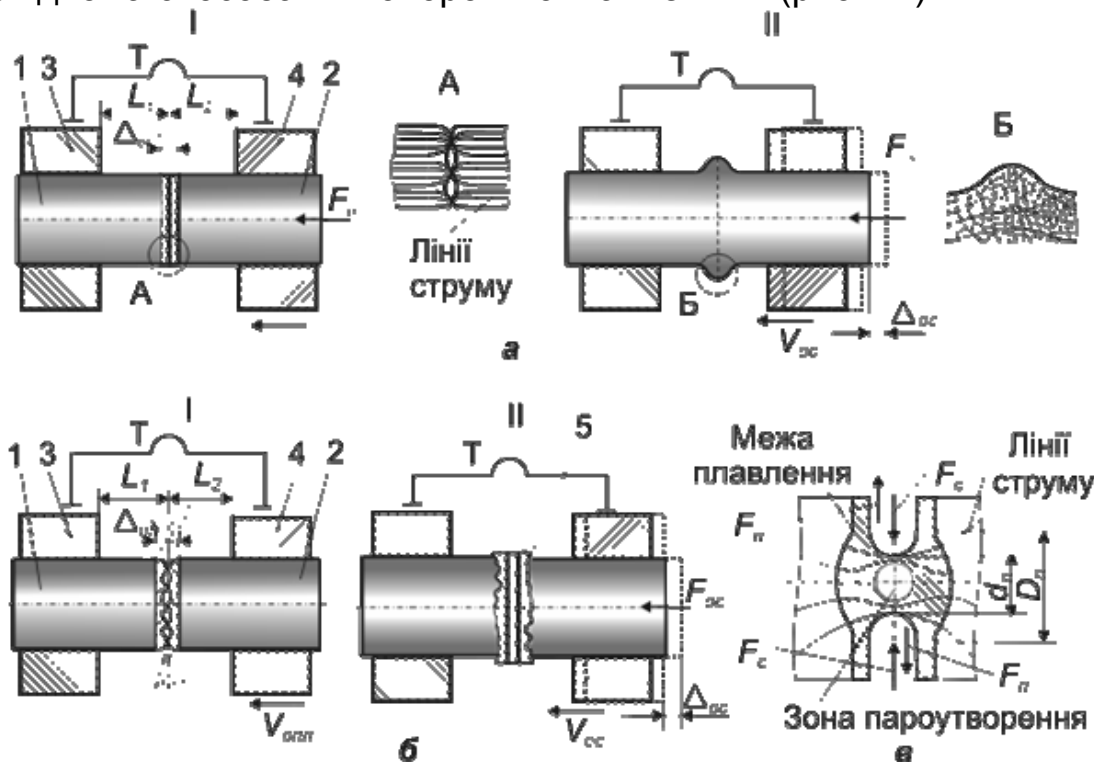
Схема стикового зварювання: а – опором; б – безперервним оплавленням; в – перемичка розплавленого металу при оплавленні; I - стик до зварювання; II - стик після зварювання
